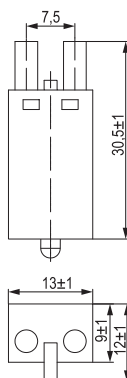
Габаритные и установочные размеры модуля / Figure 6 - Overall and mounting dimensions of the module / 6 сурет – Модулдің габариттік және орнату өлшемдері RPM-B-LD-DC6-24V,
